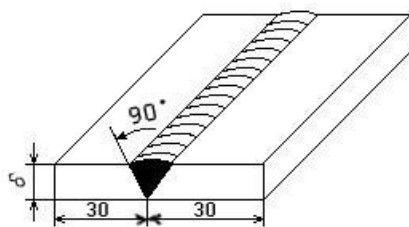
Наплавлення металу шва для вирізання зразків Гагаріна.
